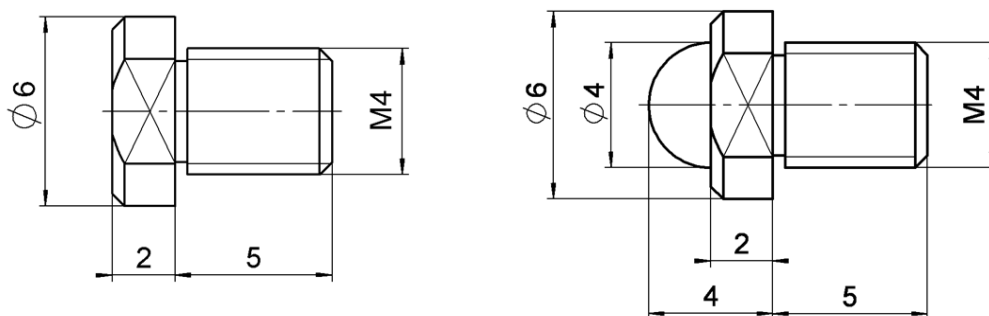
Flaches Kopfstück (links) und Kugelkopfstück (rechts); Maße in mm
